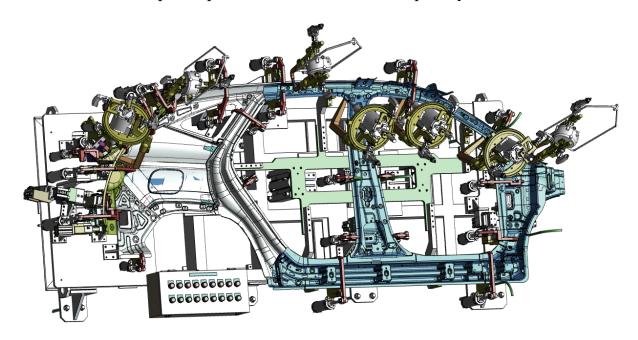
Положение сварочных пистолетов при обварке боковой панели на кондукторе
